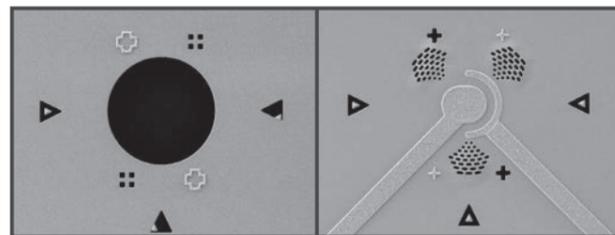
Markierungsstrukturen für die hochgenaue Flip-Chip Montage. Der Chip mit Loch (links) wird auf dem Chip mit optisch aktiver Fläche (rechts) montiert.
